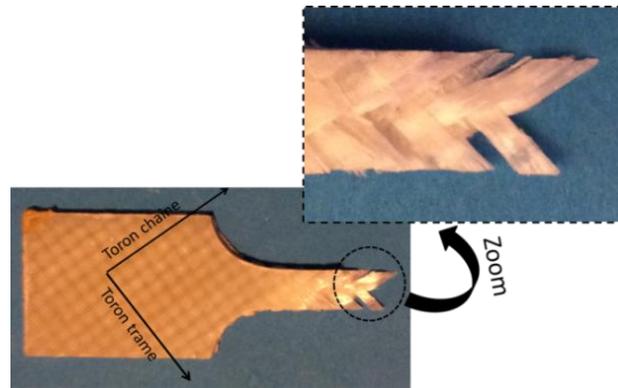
Profil de rupture d'une éprouvette taffetas de verre/Elium® sollicitée en traction par cisaillement plan.
